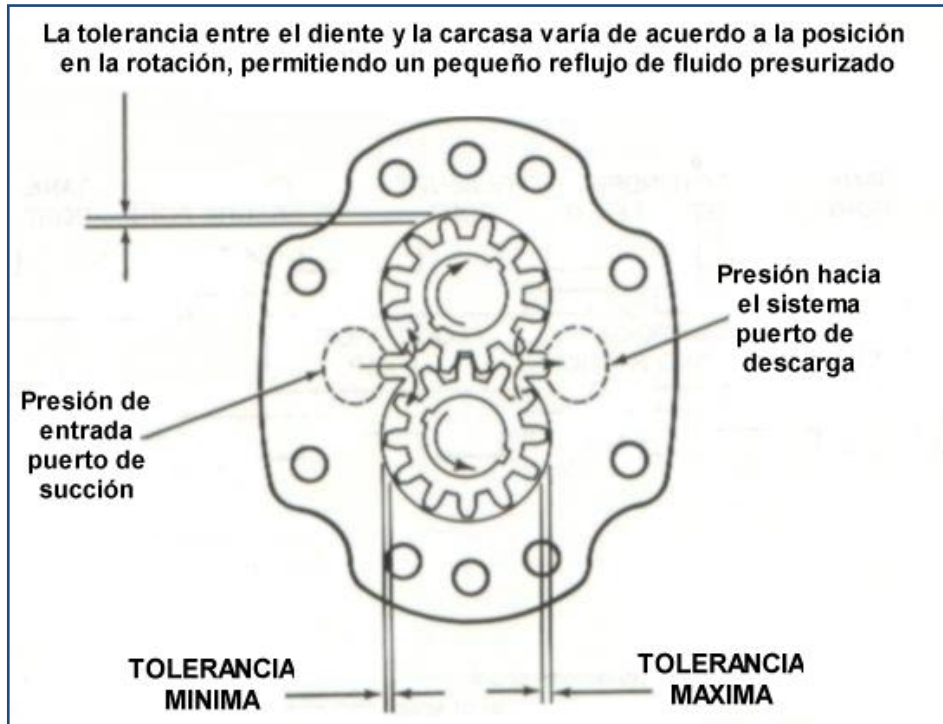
Tolerancias bombas de engranajes externos.
